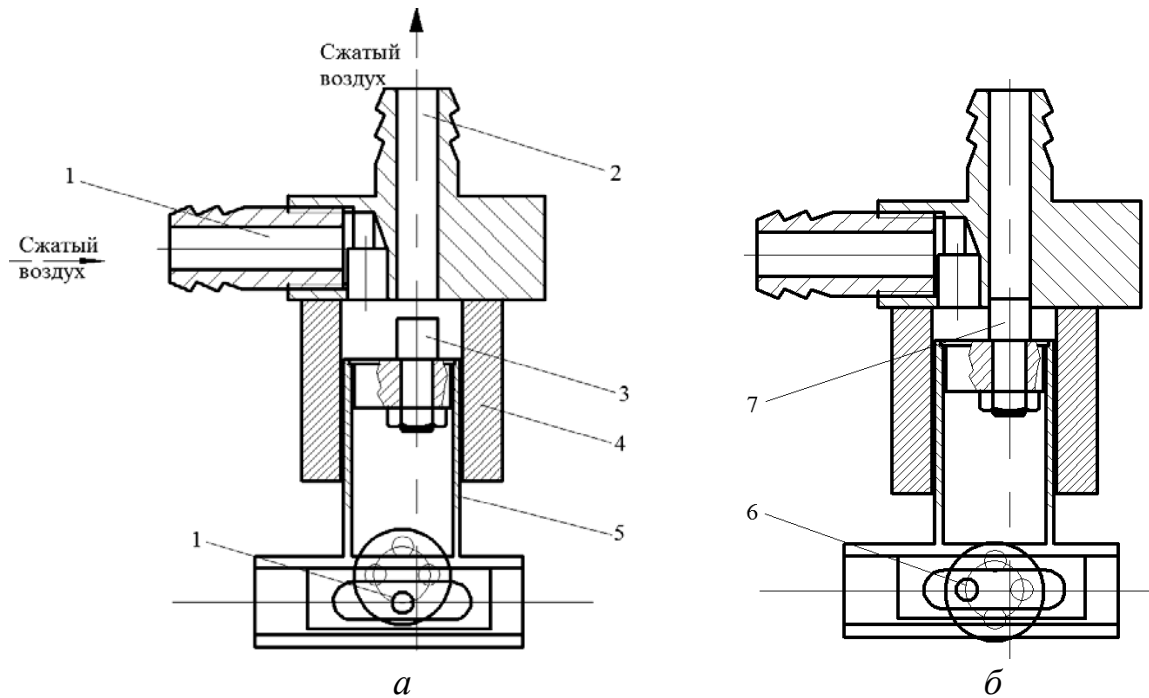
Схема устройства для прерывистой подачи сжатого воздуха с возможностью регулирования скважности и частоты подачи струй: а – кулисный механизм в нижней «мертвой» точке; б – кулисный механизм повернут на 90°.
